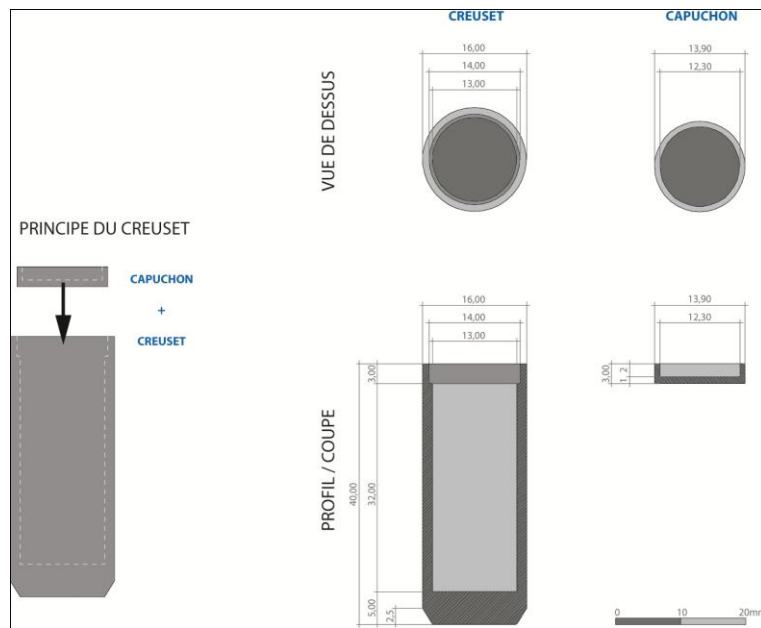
Schéma descriptif des creusets en molybdène (dimensions en mm) [2].
